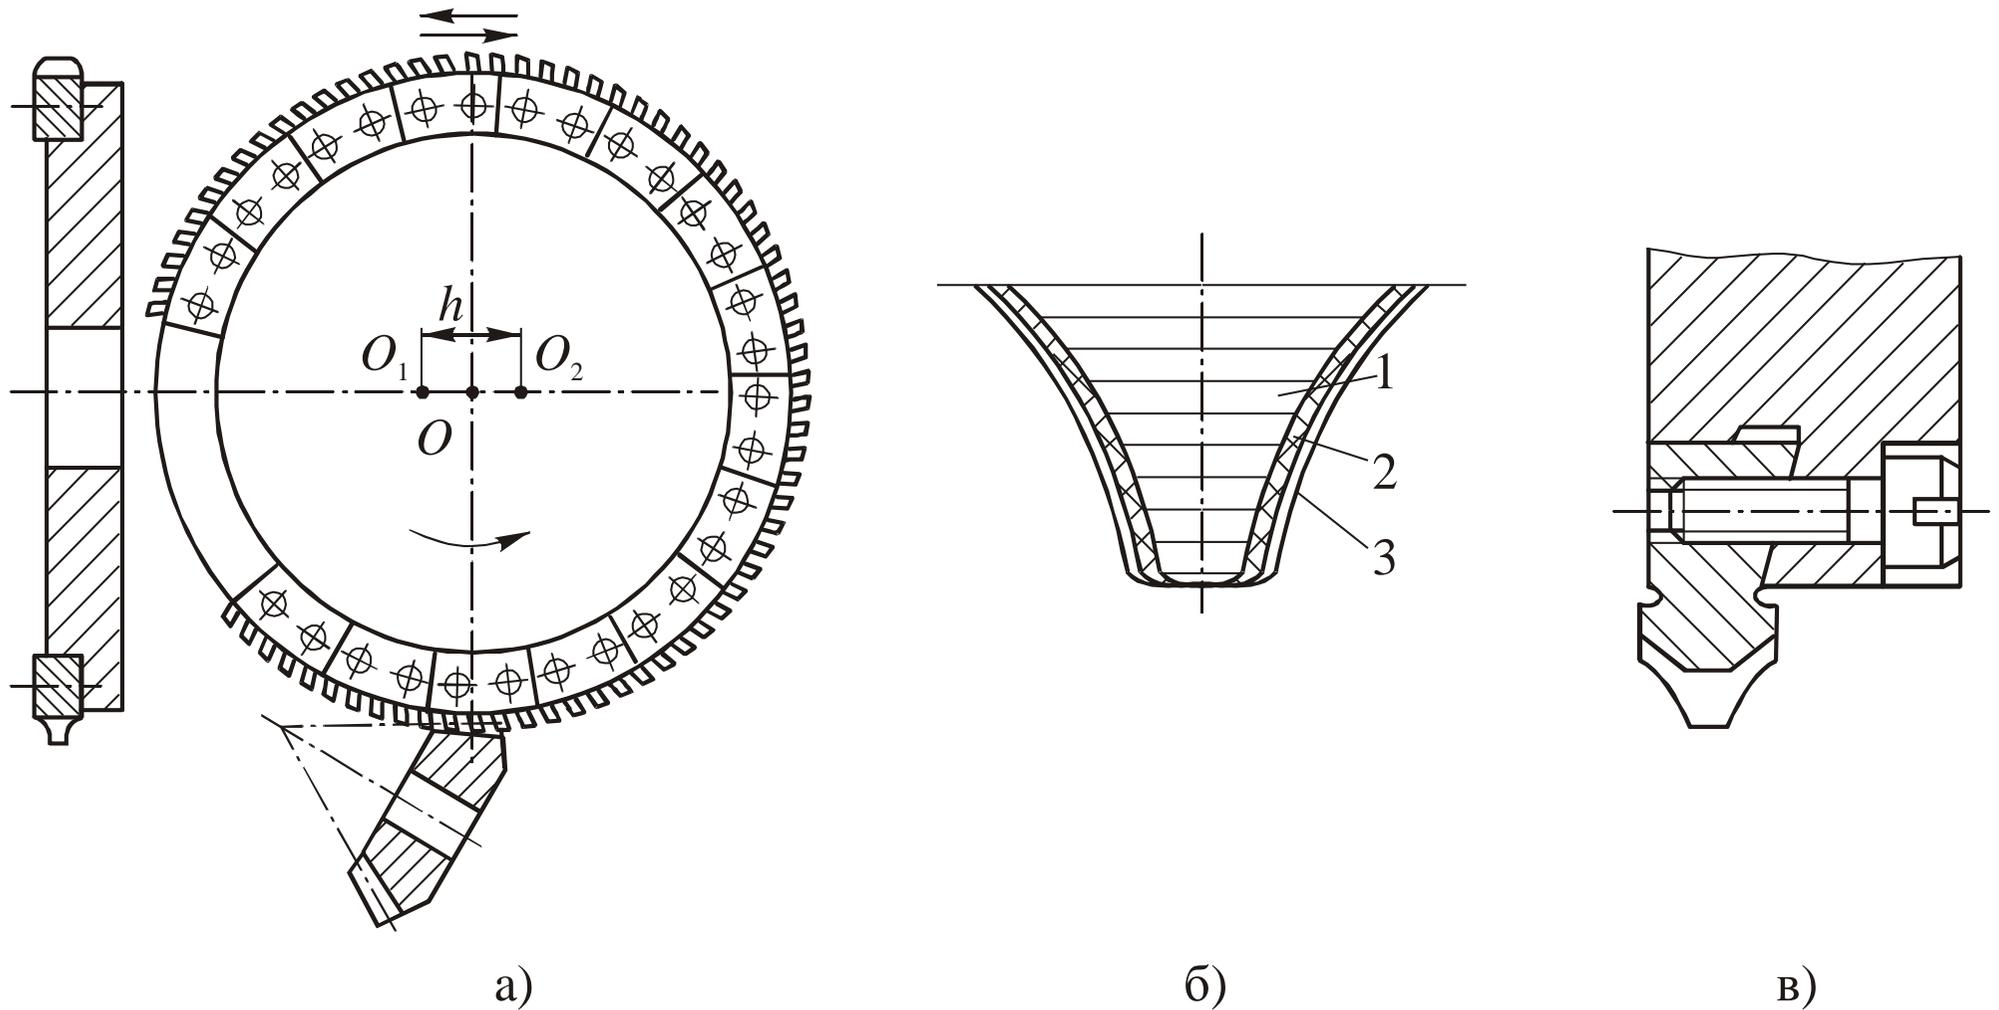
Круговая протяжка для нарезания прямозубых конических колес: *а* – конструкция протяжки; *б* – схема удаления припуска из впадины между зубьями нарезаемого колеса (*1* – черновые зубья, *2* – получистовые зубья, *3* – систовые зубья); *в* – крепление блока резцов протяжки и форма режущих кромок зубьев
